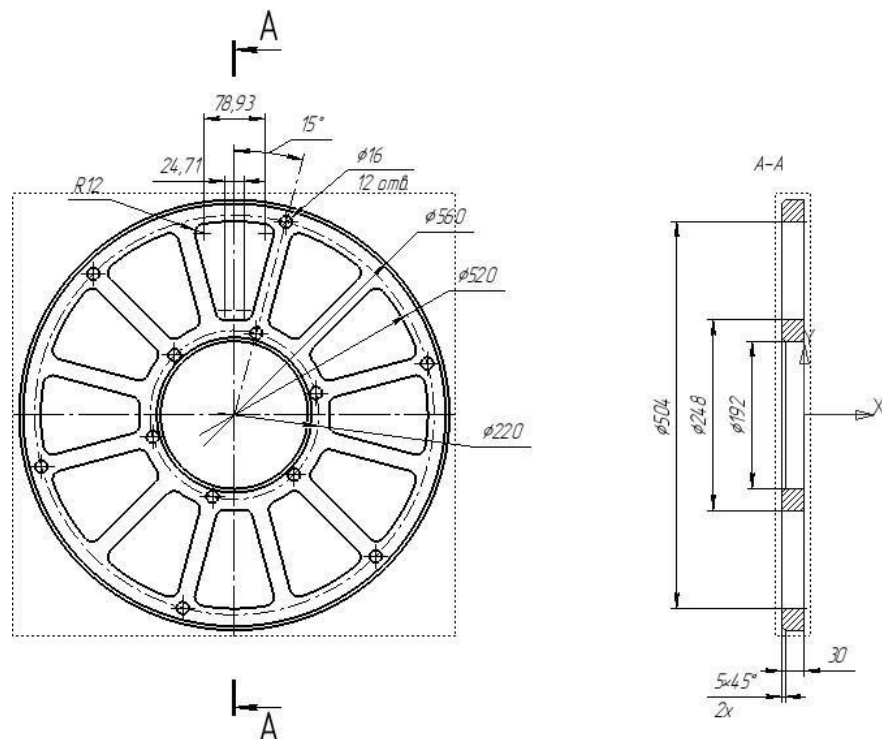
Ескіз робочої частини ячеювкої шайби
